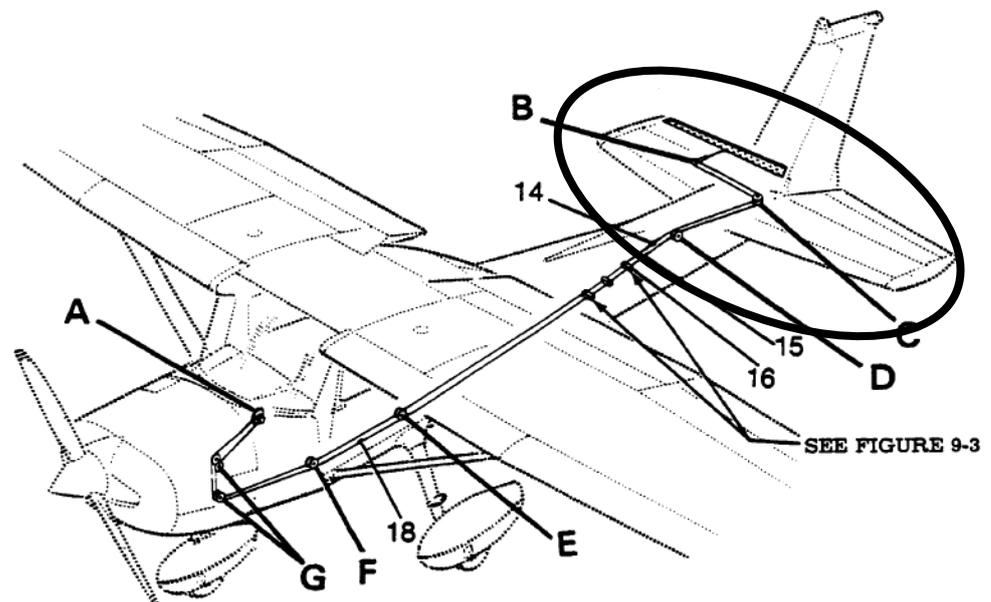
Elevator adalah kontrol primer untuk mengubah pitch pesawat
